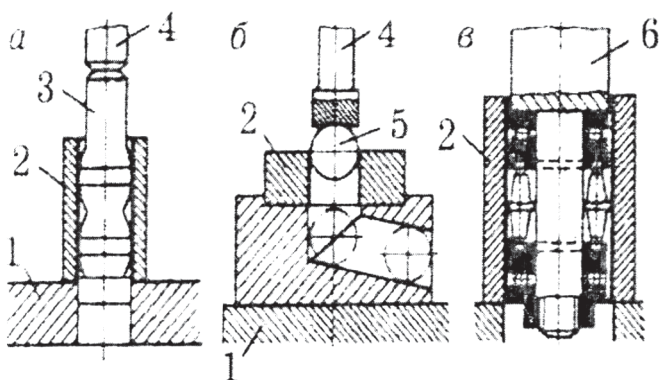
Схемы обработки отверстий без снятия стружки: а – дорнование; б – калибрование шариком; в – раскатывание роликами; 1 – стол станка; 2 – деталь; 3 – прошивка-дорн; 4 – шток; 5 – шар; 6 – раскатка
